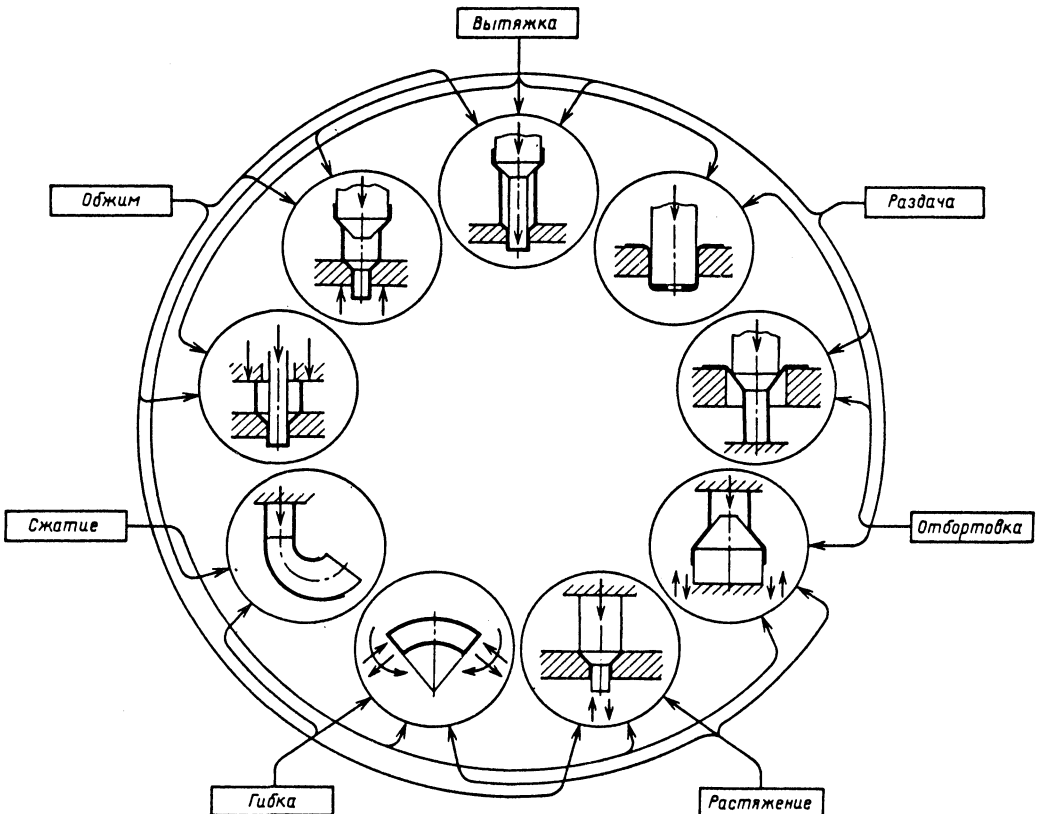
Основные совмещения формоизменяющих операций листовой штамповки
